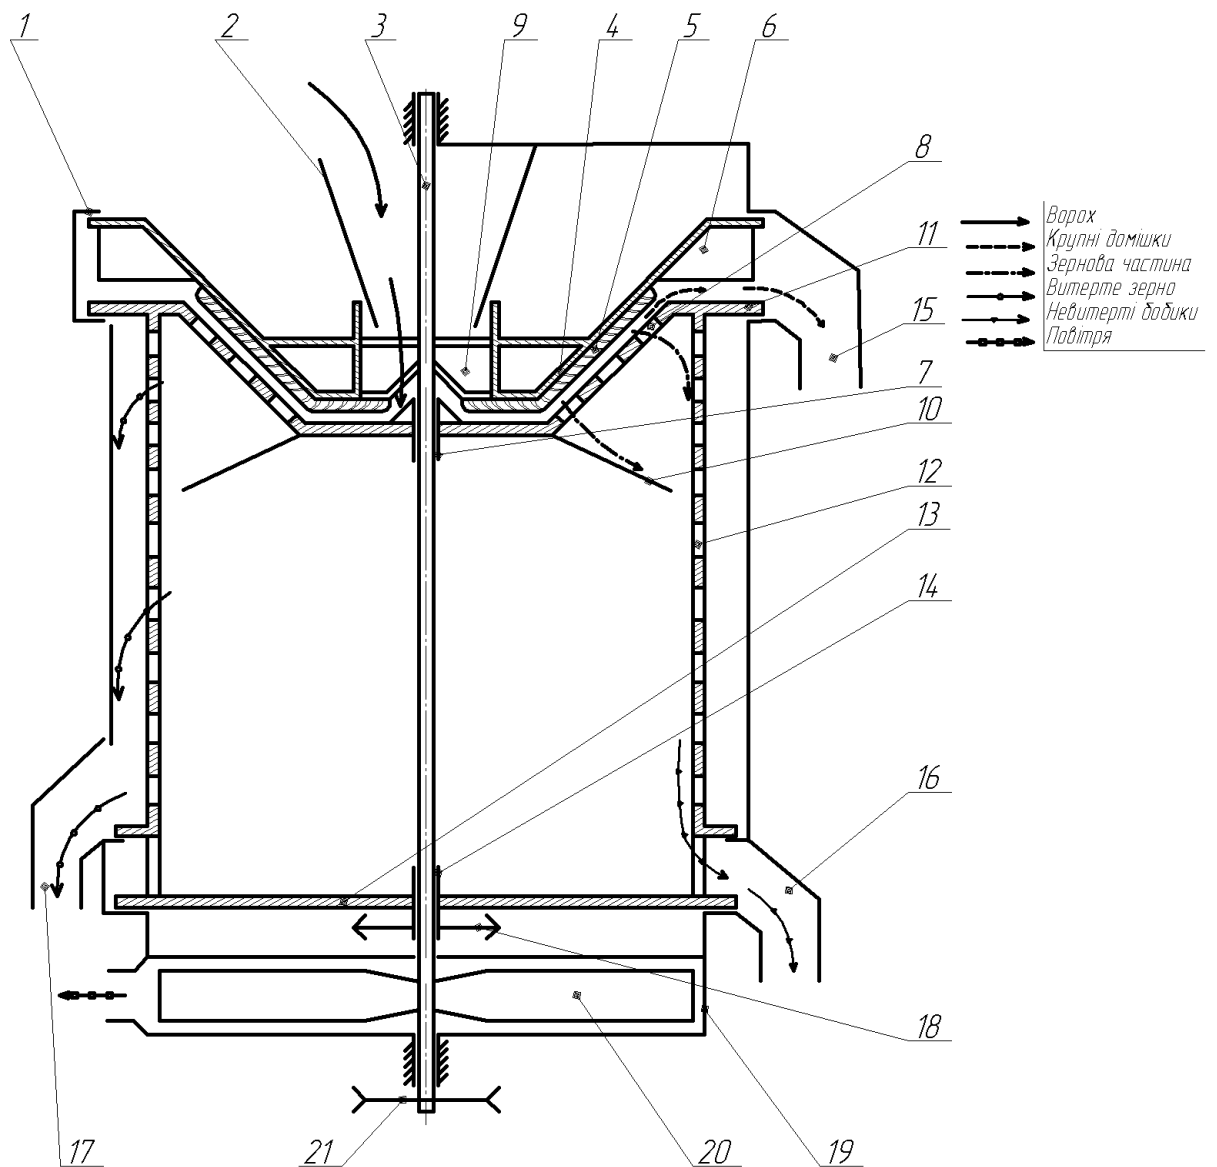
Конструктивна схема удосконаленого молотильно-сепаруючого пристрою: 1 – кожух; 2 – завантажувальна воронка; 3 – вал; 4 – конічний барабан; 5 – бичі; 6 – лопатки; 7 – підшипник; 8 – дека; 9 – скребки; 10 – розсіюючий конус; 11 – кільце; 12 – циліндричне решето; 13 – диск; 14 – підшипникова опора; 15 – канал для відводу солом'яної частини вороху; 16 – канал для відводу не витертого із бобів зерна; 17 – канал для відводу очищеного насіння; 18 – автономний привід; 19 – вентилятор; 20 – лопаті; 21 – привод.
